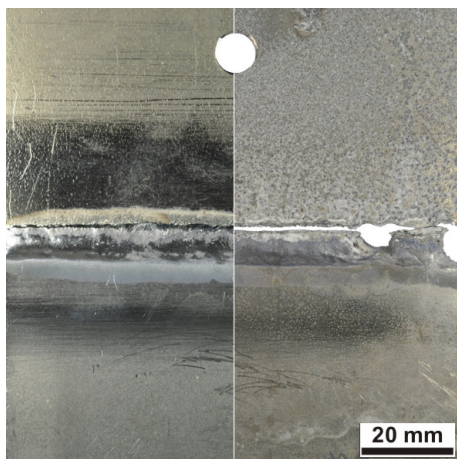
Unbeschichtetes Versuchsblech der geschweißten Verbindung AZ31 / AA6016 / AlSi12, links: Ausgangszustand, rechts: Versuchsblech nach einer Woche Korrosionsprüfung nach VDA 621-415, Bruch entlang der Magnesiumanbindung an die Schweißnaht
